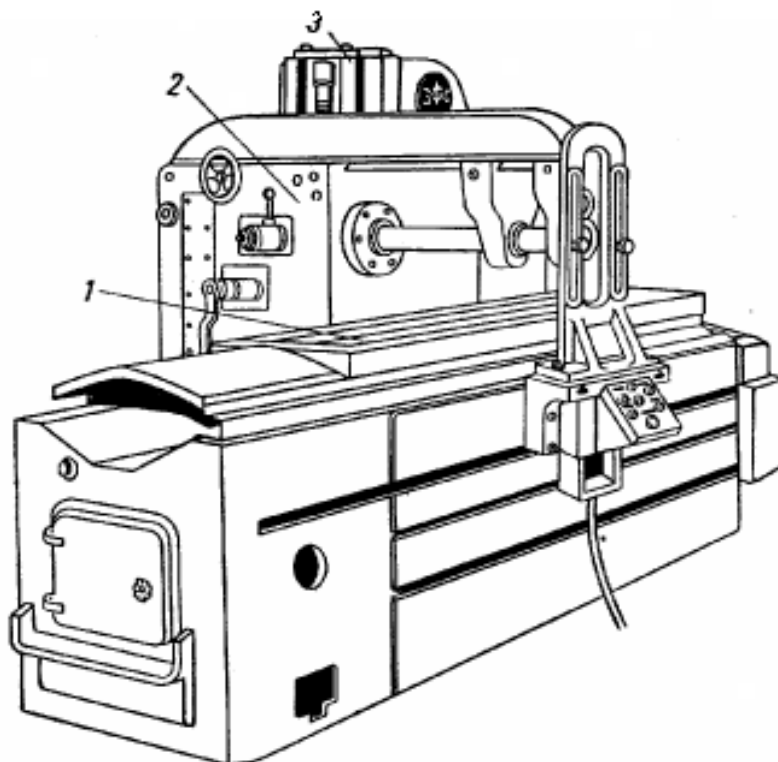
Одностоечный продольно-фрезерный станок с одним горизонтальным шпинделем А662В:
